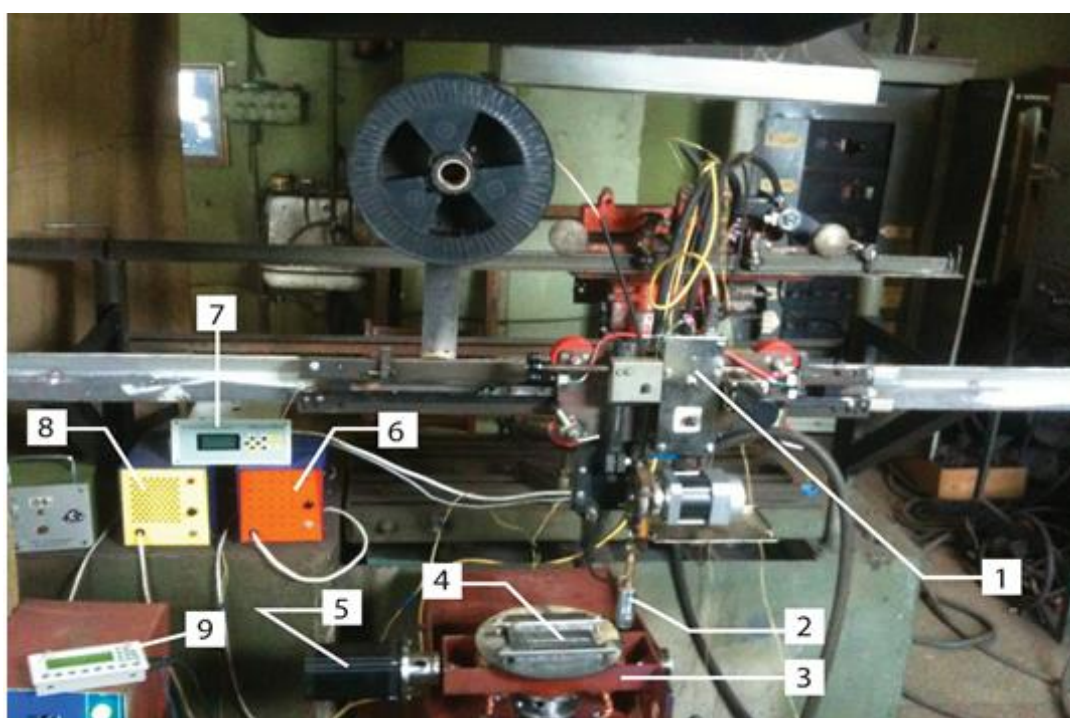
Структурна схема установки для наплавлення: 1 – рухома станина; 2 – зварювальний пальник; 3 – коливальний стіл; 4 – деталь що наплавляється; 5 – кроковий двигун; 6, 8 – електричні перетворювача; 7 – електронний індикатор швидкості подачі зварювального дроту; 9 – пульт керування кроковим двигуном
